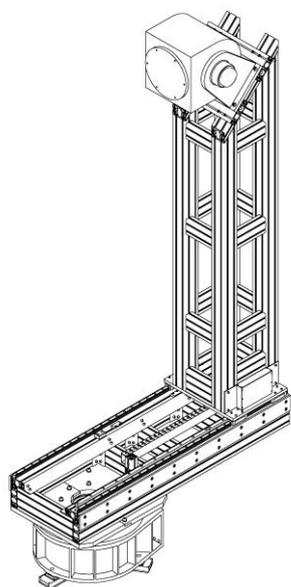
Общий вид четырехкоординатного опорно-поворотного устройства
